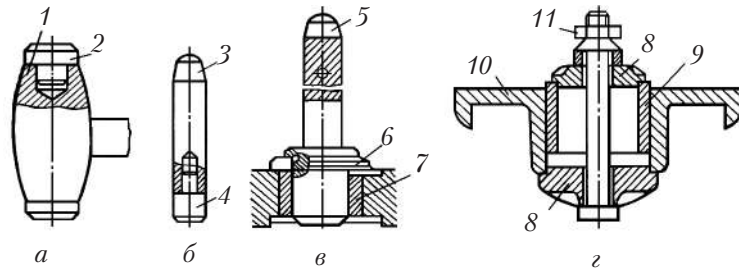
Інструменти та пристосування для складання пресових з'єднань: а – молоток із вставним бойком; б – вибивач; в – оправка; г – гвинтове пристосування; 1 – молоток; 2 – вставний бойок; 3 – стрижень; 4 – змінний наконечник; 5 – оправка; 6 – кільце; 7, 9 – втулки; 8 – шайба; 10 – корпус; 11 – гайка
